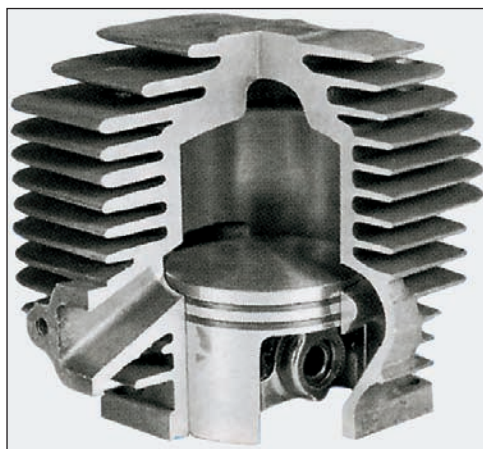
Цилиндр и поршень двухтактного двигателя воздушного охлаждения
